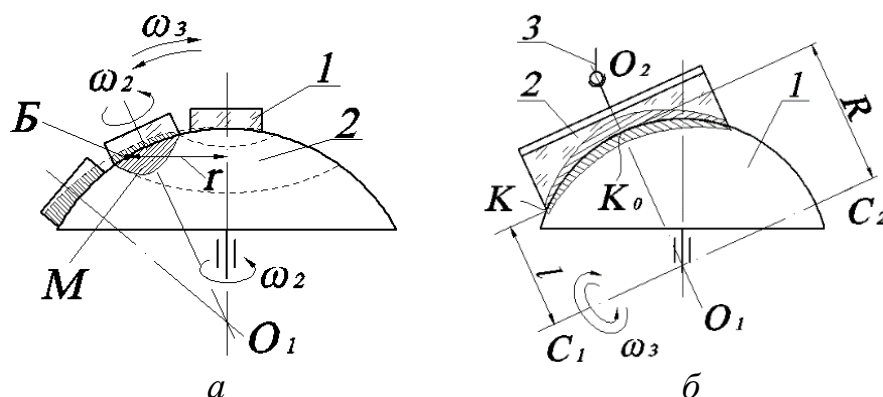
Распределение эпюр срабатывания при поступательном перемещении заготовки со сферической поверхностью
